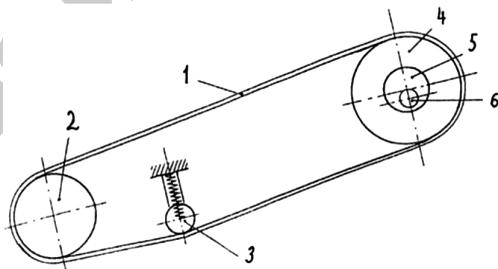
Устройство для сепарации корнеплодов (вид сбоку)
